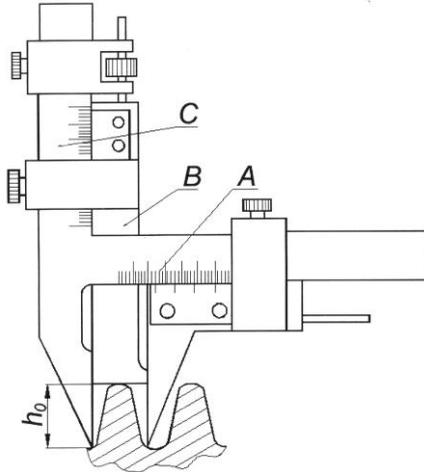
Схема измерения высоты профиля зуба в нормальном сечении с помощью штангензубомера
